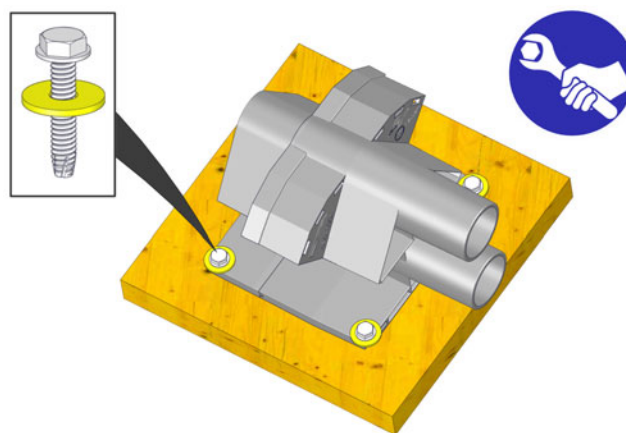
Sonde d'aspiration sur une planche de bois
